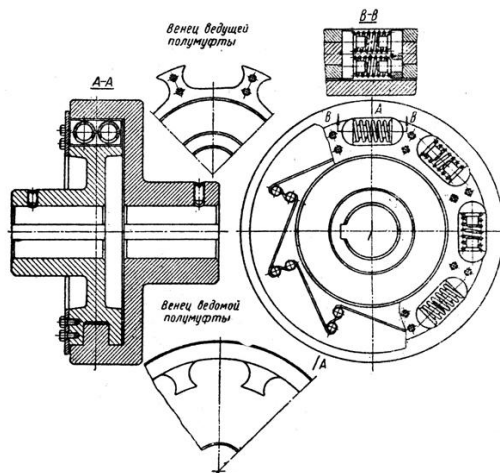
Муфта упругая с цилиндрическими винтовыми пружинами
